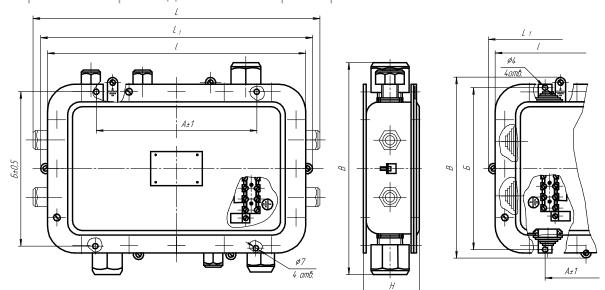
Коробки с привертными сальниками (пластмассовый)
